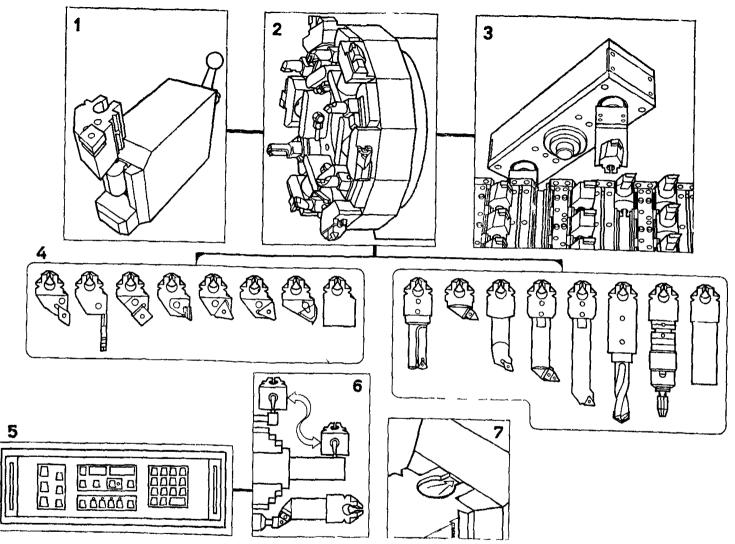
Пример установления стандартных присоединительных поверхностей обеспечивающих единство блочно модульного метода агрегатирования в ЦКИ для станков токарной группы
